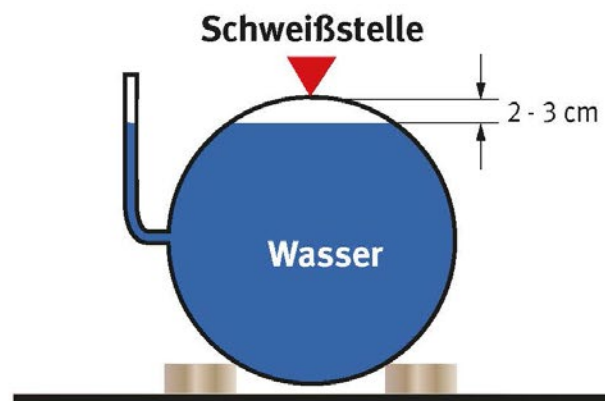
Arbeitstechnik beim Schweißen von Fässern oder ähnlichen Hohlkörpern
